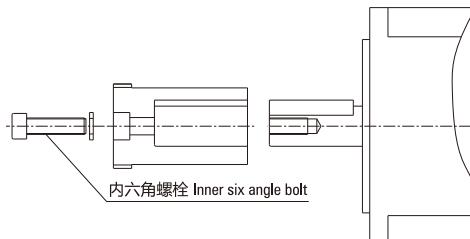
表示伺服电机轴的形状和输入齿轮的安装示例，请参照此图进行设计。
